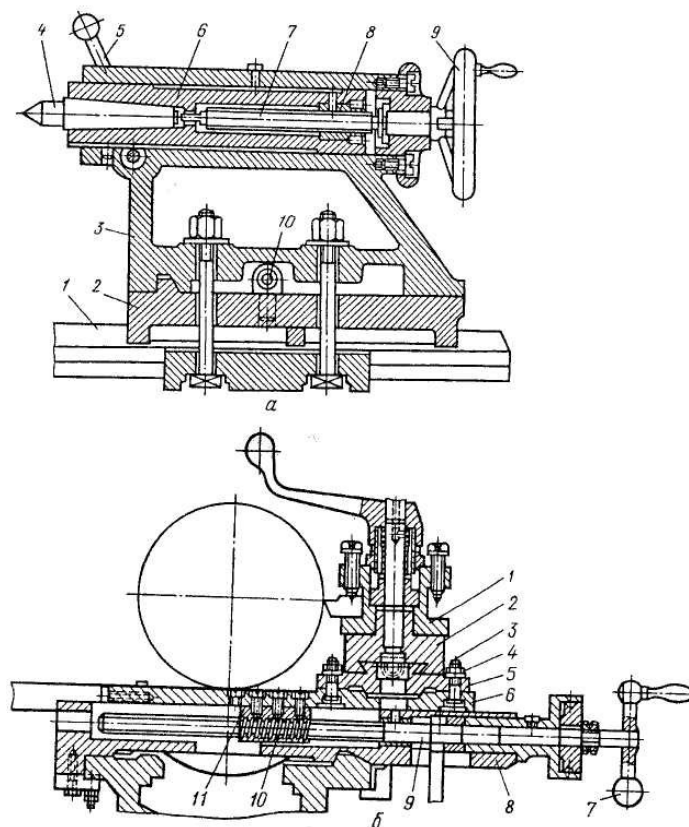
Схемы задней бабки (а) и суппорта (б) токарно-винторезного станка
